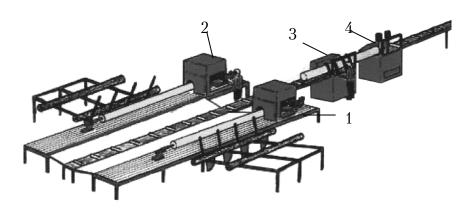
Технологическая линия по производству деталей домов из оцилиндрованного бревна: 1 — механический подъемник бревна; 2 — оцилиндровочный станок; 3 — чашкорезный станок; 4 — торцовочный санок
